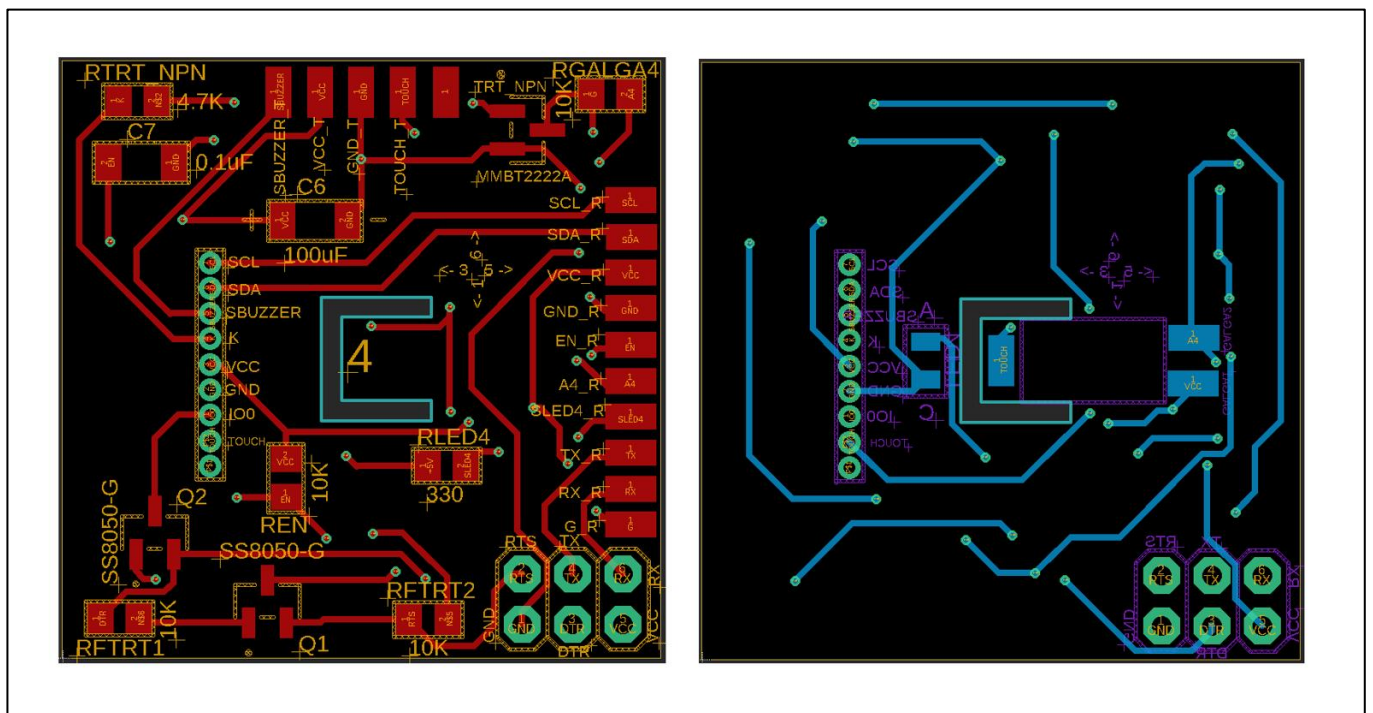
PCB de la Cara 4. Capas TOP y BOTTOM.
